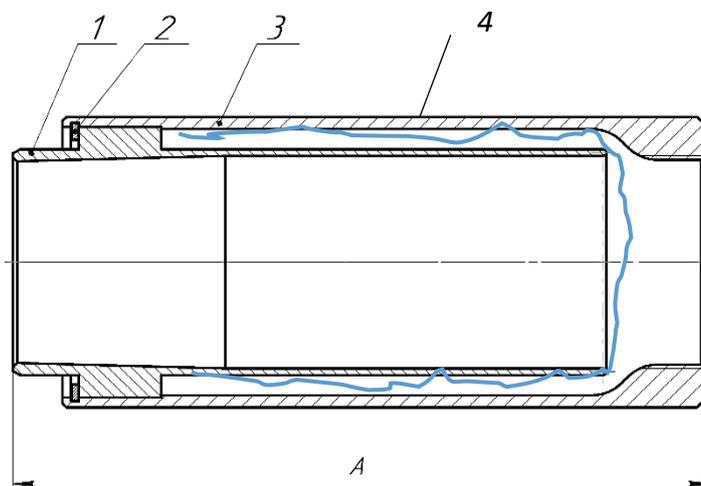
Керноупаковочная кассета. (Керноупаковочное приспособление) в сборе
